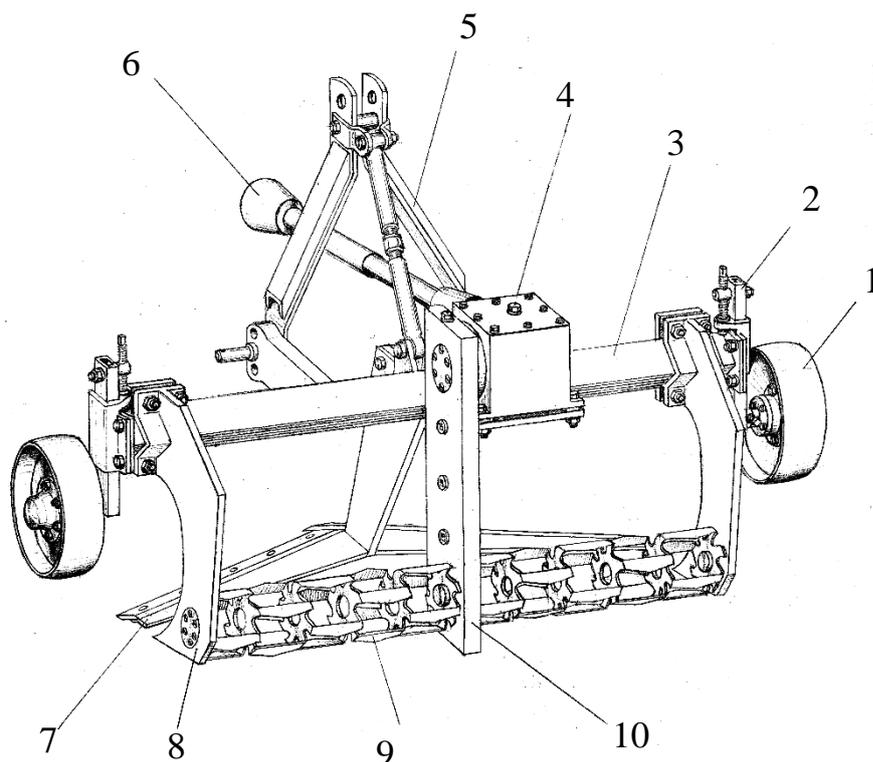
Схема комбинированного подпокровного фрезерователя:
